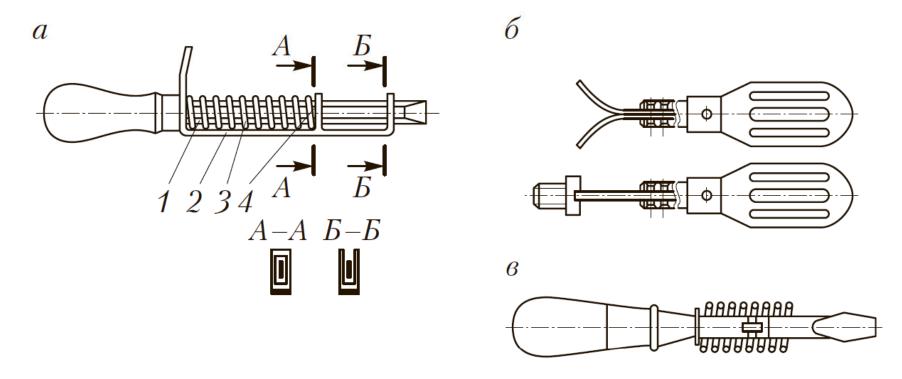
Отвертки для работы в труднодоступных местах: а — с вильчатым захватом (1 — стержень отвертки; 2 — планка; 3 — пружина; 4 — штифт); б — с плоскими пружинами; в — с изгибающимся стержнем
